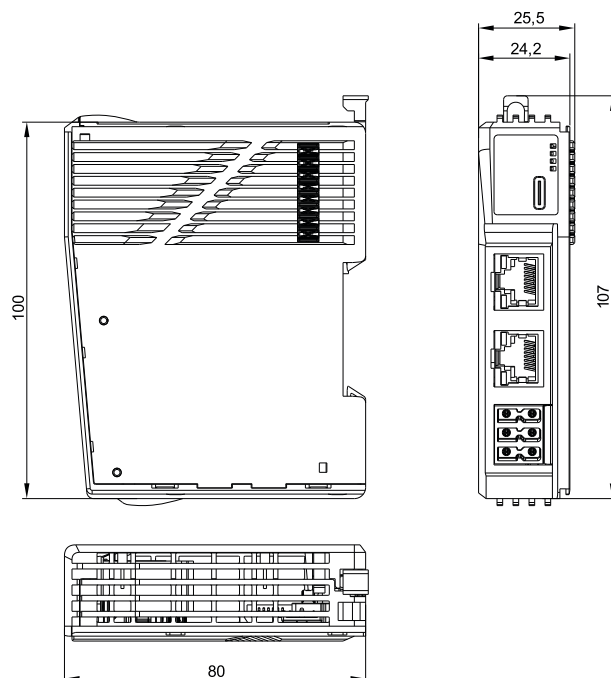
Габаритные и установочные размеры соединительного модуля
